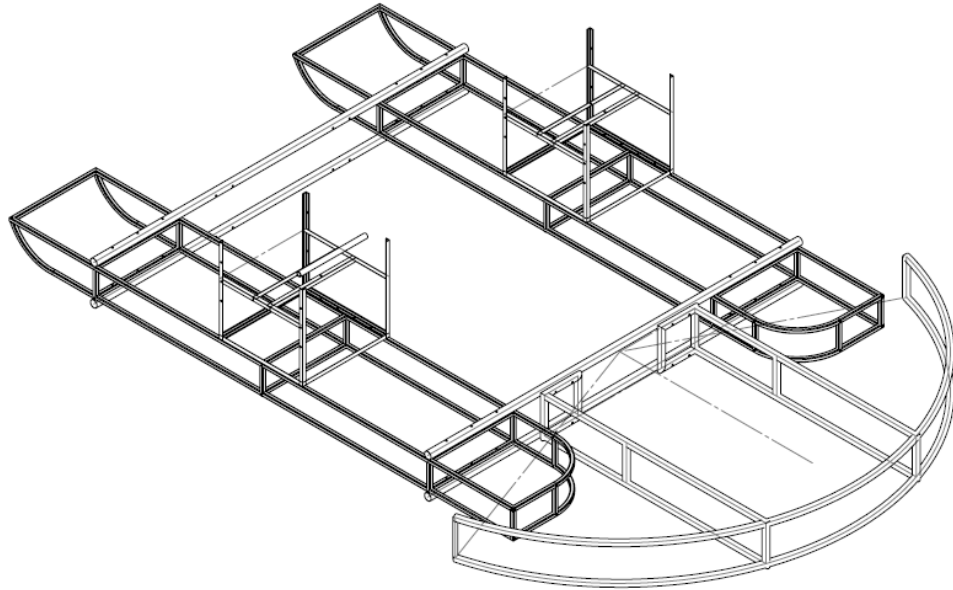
Defensa triangular sobre estructura soporte (primera alternativa) laminado
